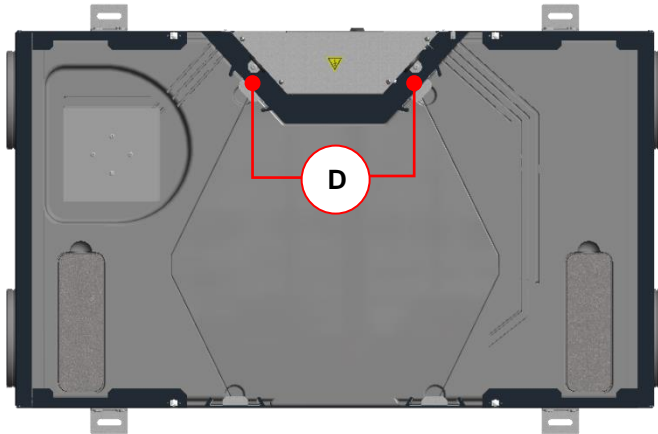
Schrauben D zur Fixierung des Steuerungsgehäuses
